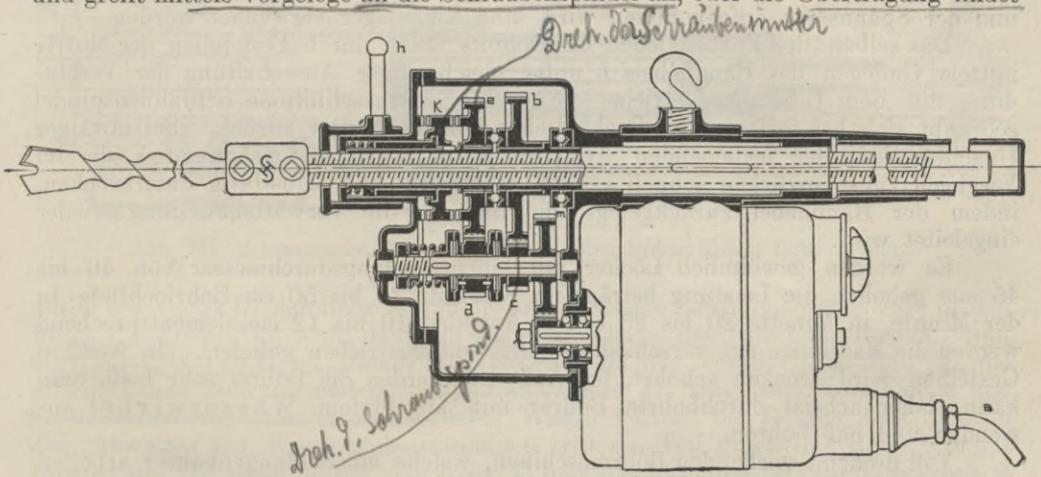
Elektrisch angetriebene, drehend wirkende Bohrmaschine von Siemens und Halske.
